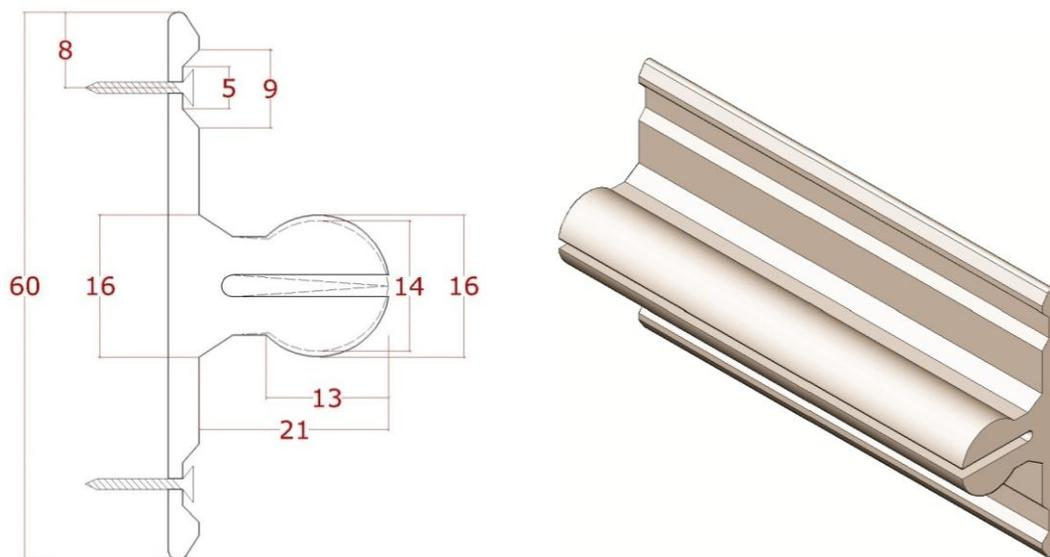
Profilato di supporto. Particolare della sezione con misure espresse in millimetri e vista 3D.
